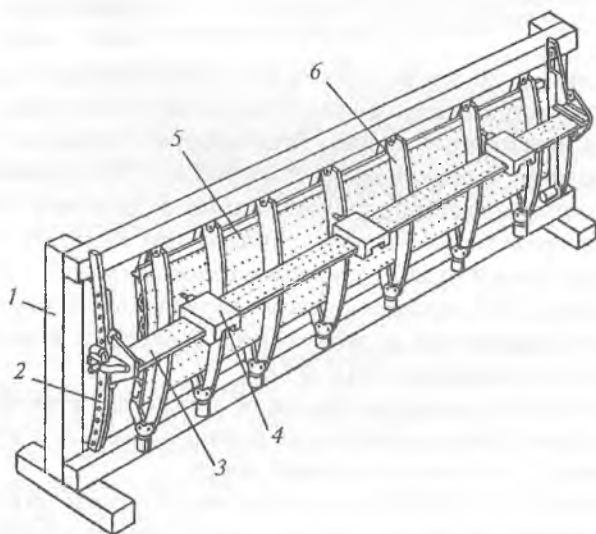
Сборочное приспособление, оснащенное агрегатами СЗА-02: 1 — сборочное приспособление; 2 — копир по обводам панели; 3 — траверса; 4 — агрегат СЗА-02; 5 — панель; 6 — рубильники
